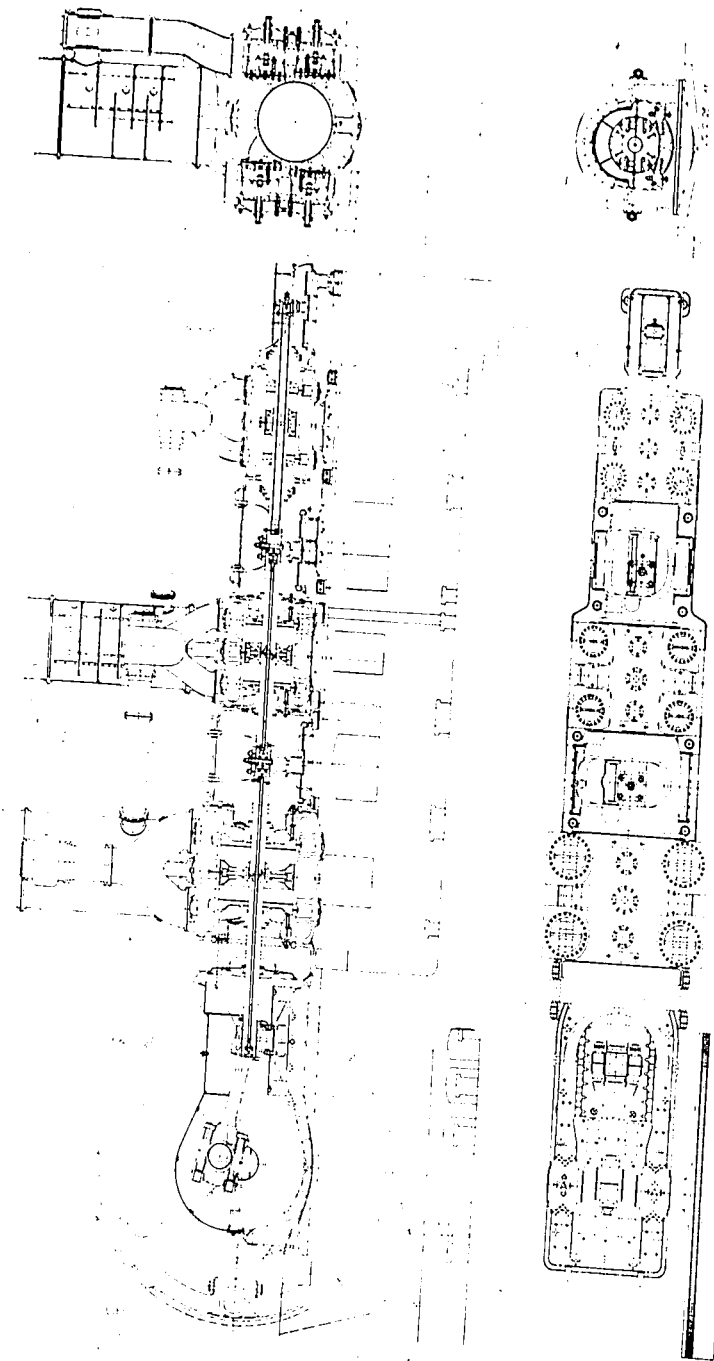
6 dreistufige Hochdruck-Mischgas-Kompressoren in Zwillingsanordnung, geliefert für ein Stickstoffwerk, gekuppelt mit je einer Generatorgas-Tandemaschine. Ansaugmenge std. je Kompressor 17 000 m³, Druck 30 atü, Drehzahl min. 94,35.
